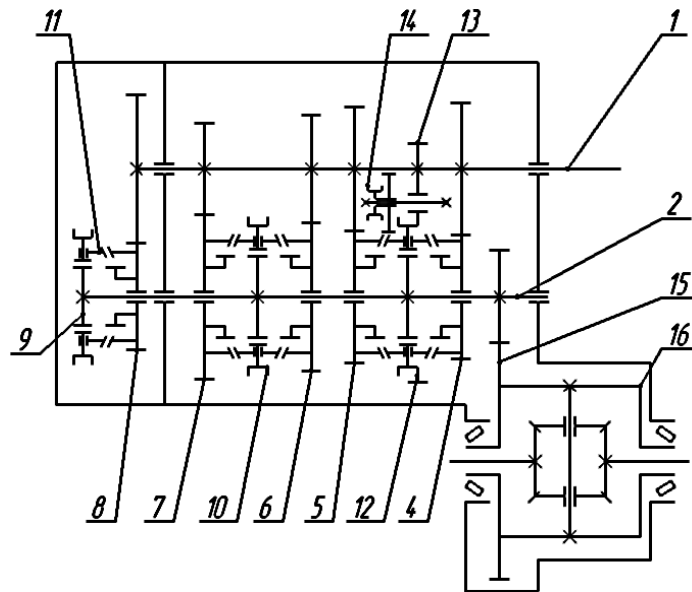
Кинематическая схема двухвальной коробки перемены передач:
